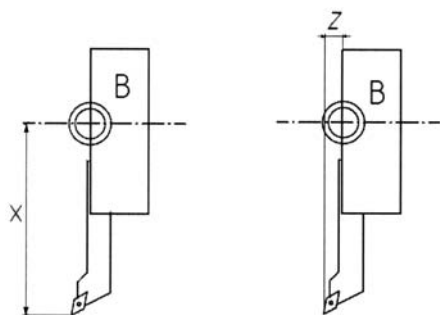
Длина инструмента по оси X и Z (для резцов)
